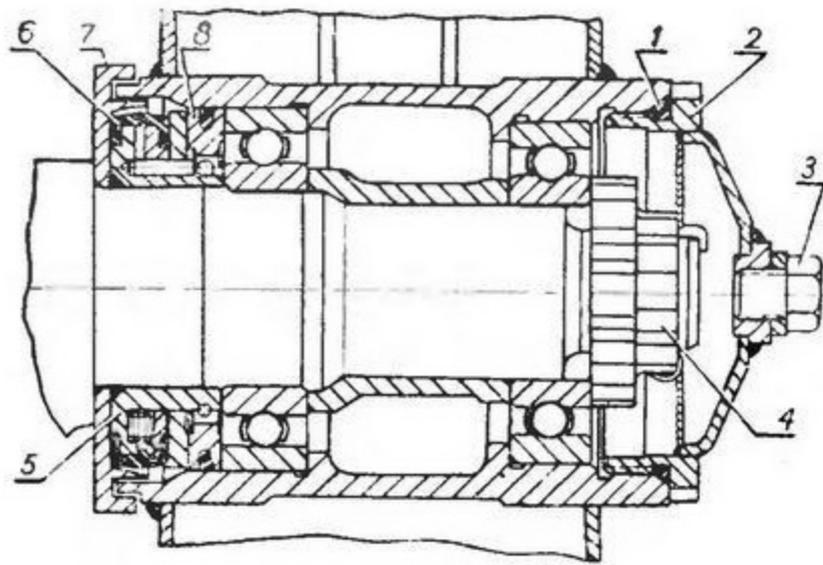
Уплотнение подшипников ступиц катков и ленивцев.
